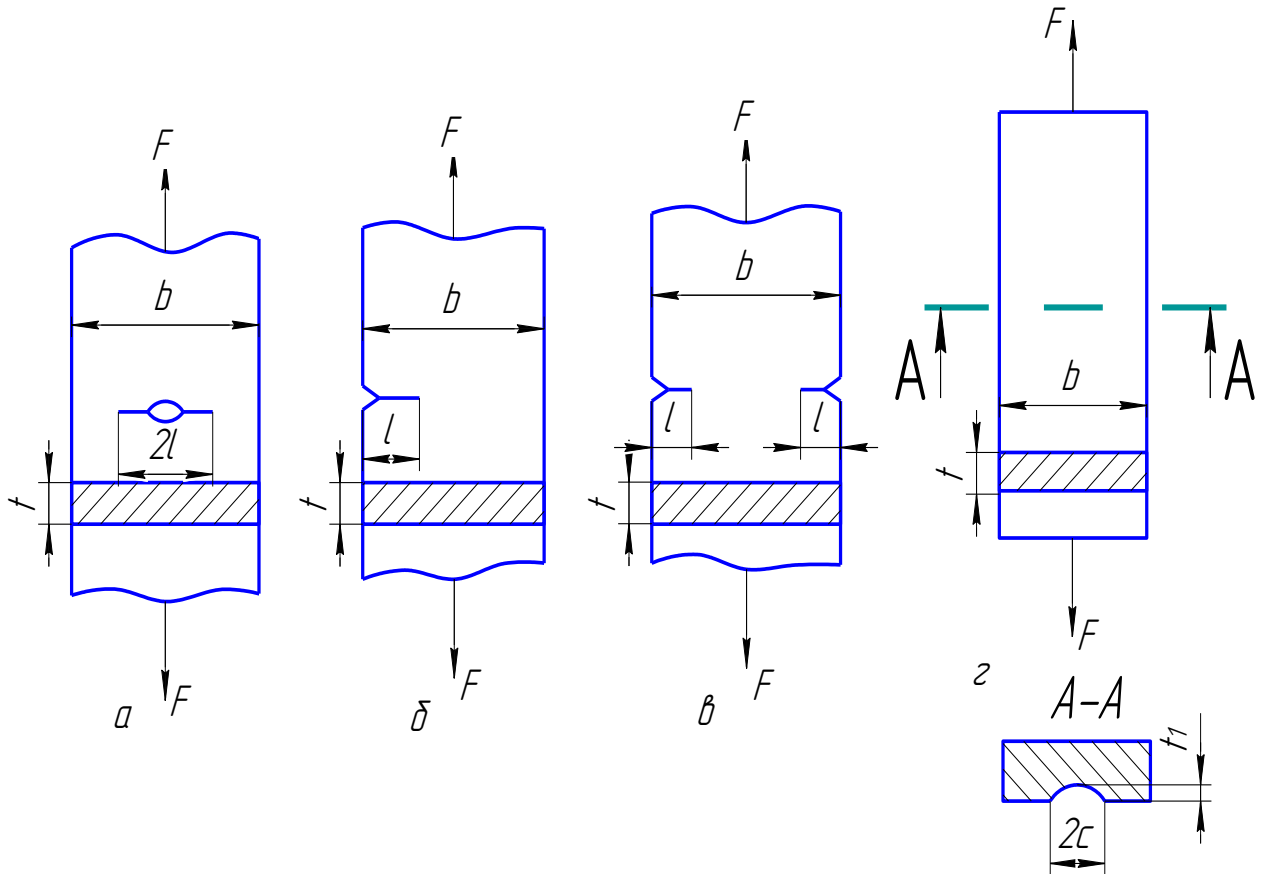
Зразки пластини на розтяг: а) – з центральною тріщиною; б) – з боковою тріщиною; в) – з двома боковими; г) – з поверхневою сегментною.
